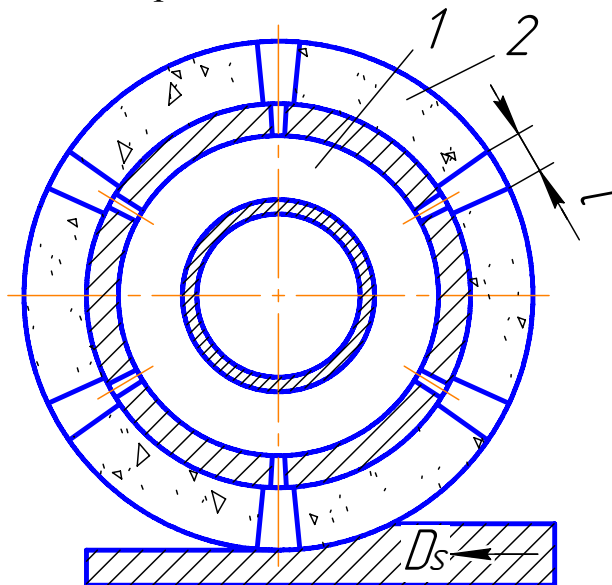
Сборный шлифовальный круг с дискретной режущей поверхностью, работающий периферией
